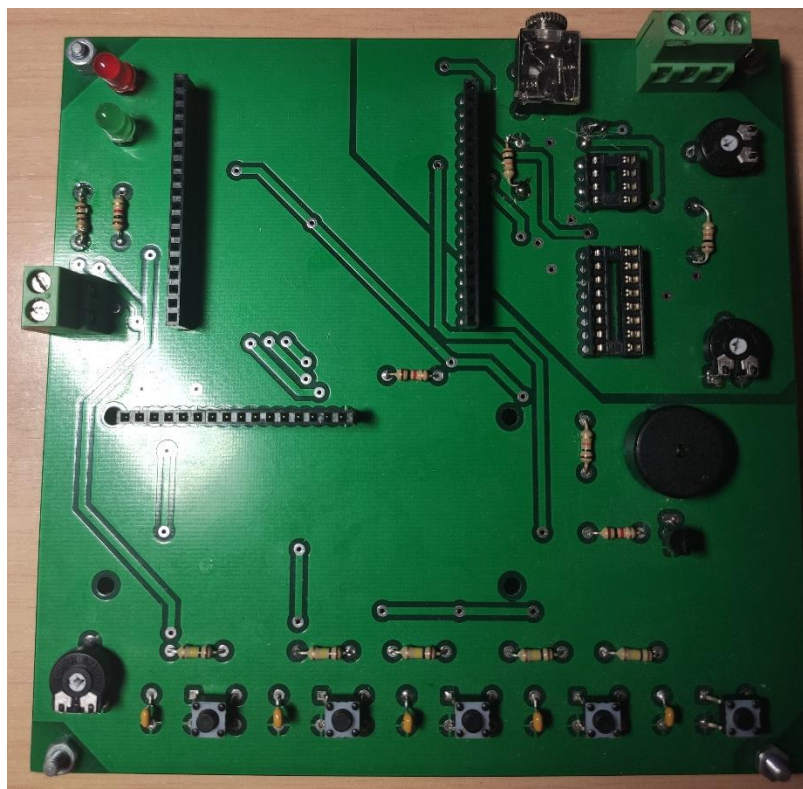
Estat de la cara superior un cop s'ha realitzat el procés de soldadura.
